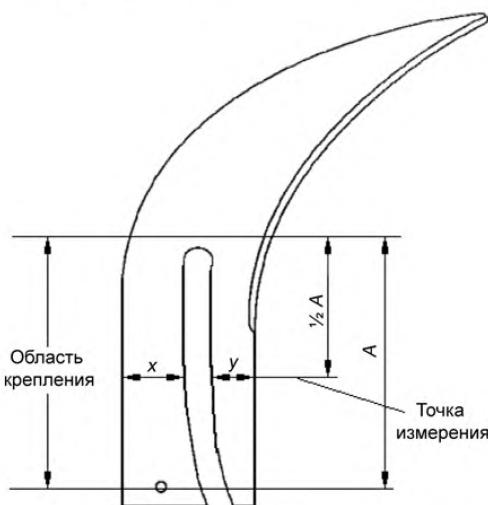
Ширина расклинивающего ножа в области крепления
